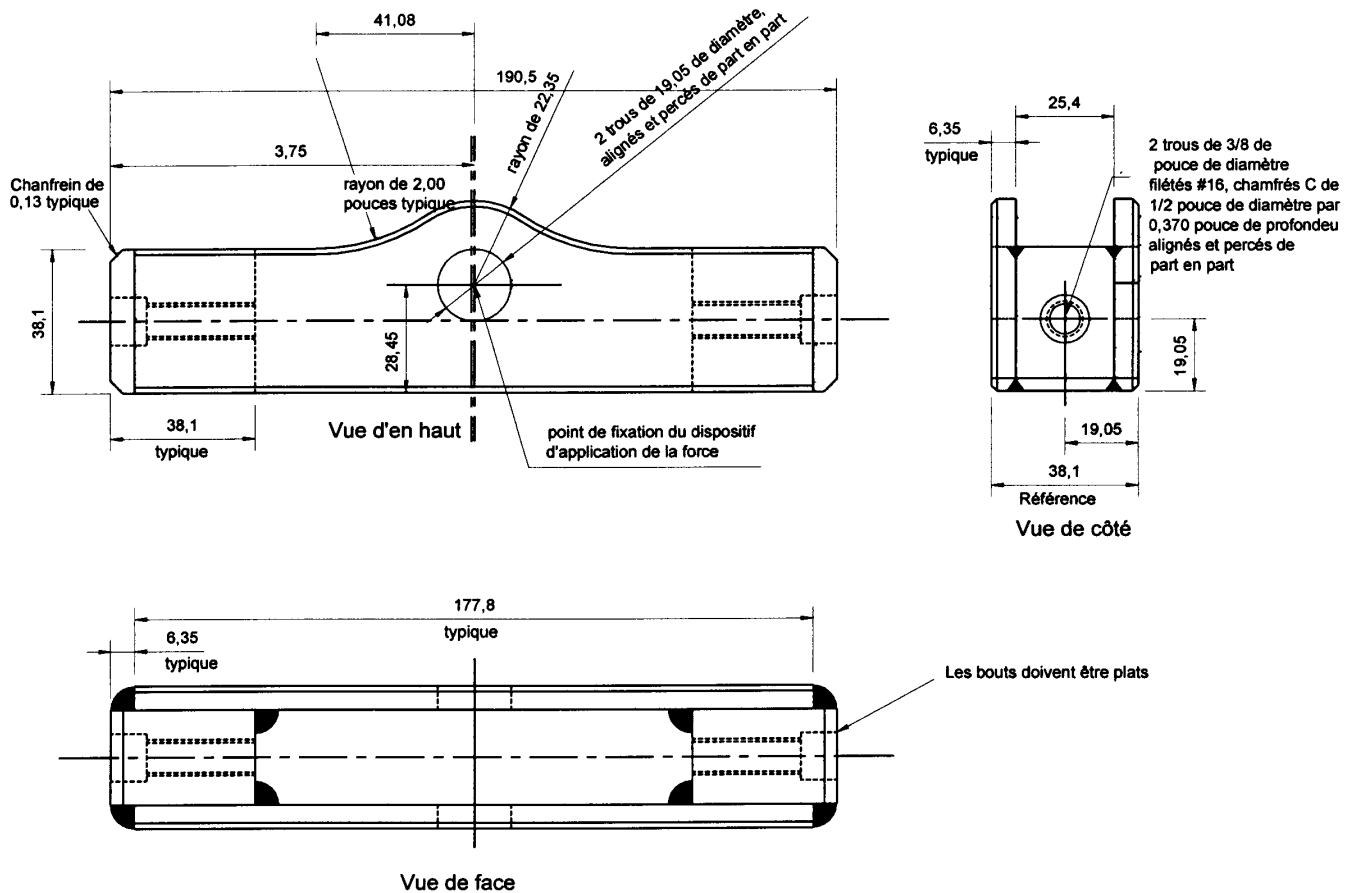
Vue en plan du dispositif d'essai d'application de la force statique
